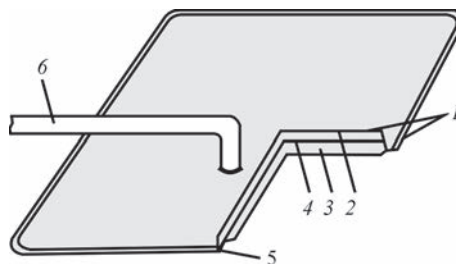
Сборка для пайки: 1 — полужесткая форма кассеты; 2 — защитное покрытие; 3 — основной металл, имитирующий панель кристаллизатора; 4 — припой; 5 — герметизирующий сварной шов; 6 — патрубок для вакуумирования
